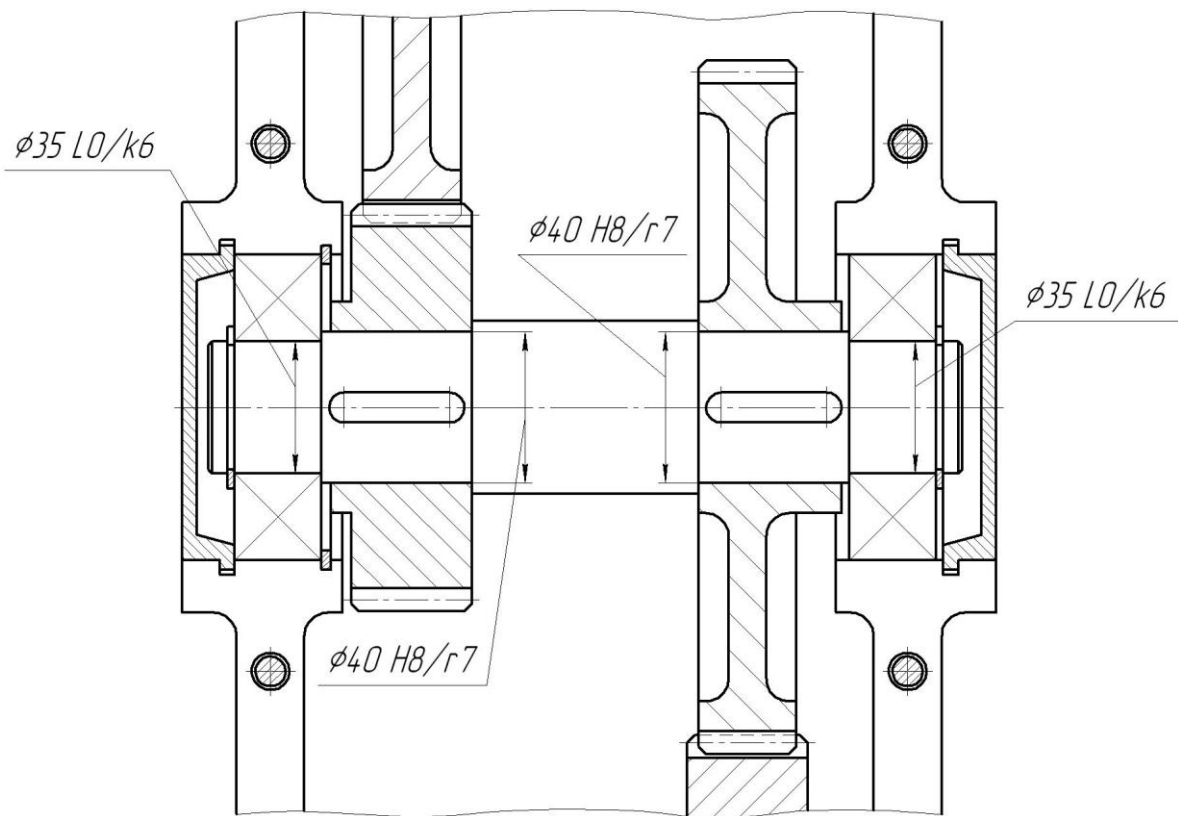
Конструктивна схема вузла проміжного вала
